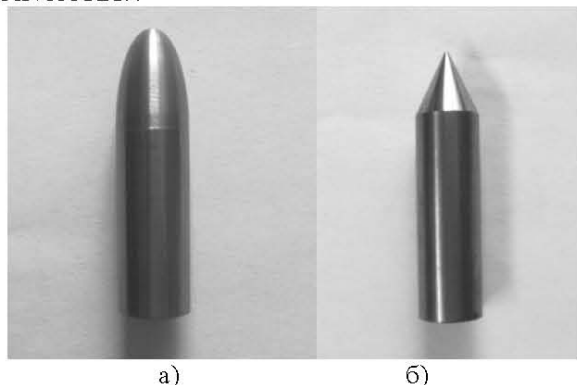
Пуансон-сверло (а - с криволинейной формой рабочей части; б - с конической формой рабочей части)
